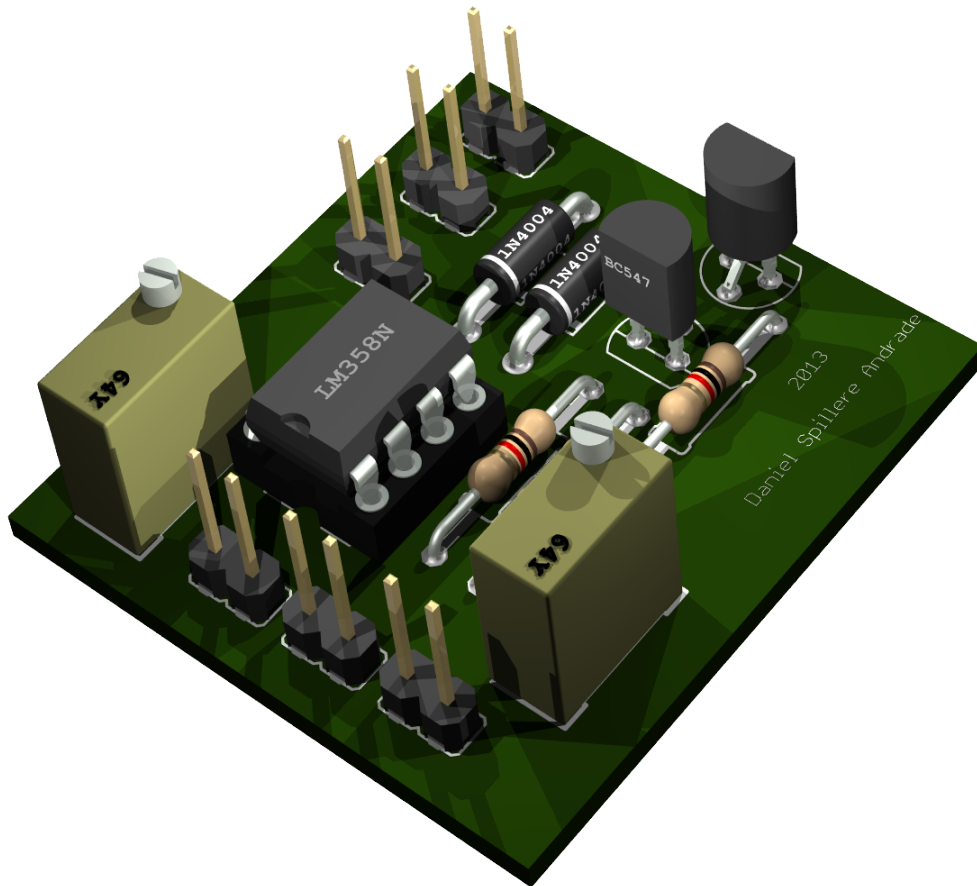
Simulação 3D da placa de circuito impresso com os componentes soldados.
